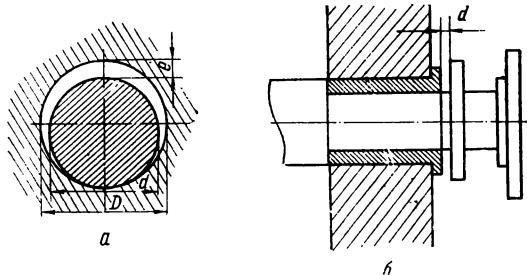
Масляные зазоры в соединении вала и втулки (подшипника) скольжения
